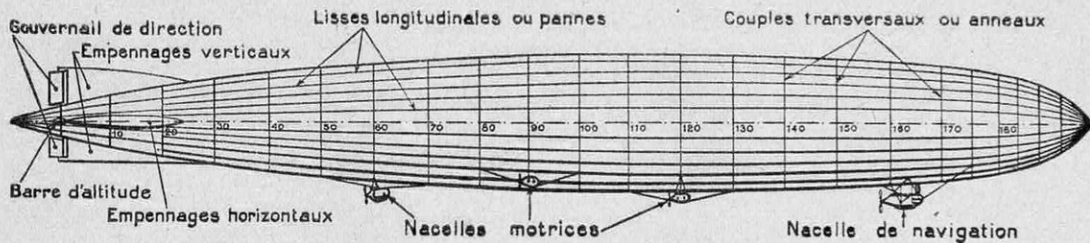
COUPE LONGITUDINALE VERTICALE DU « LOS-ANGELES »
